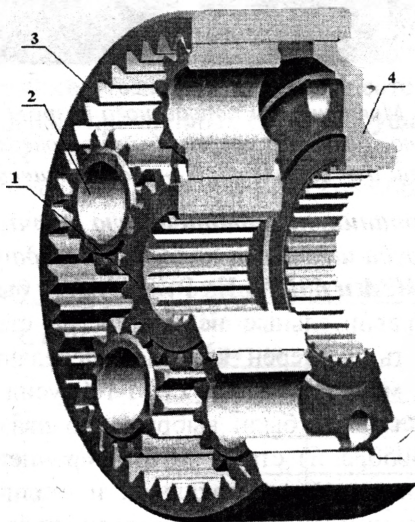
Планетарная колесная передача автомобиля МАЗ. 1 — ведущая шестерня; 2 — сателлит; 3 — ведомая шестерня; 4 — ступица
